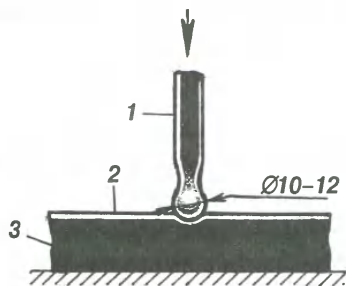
Вытягивание сферы: 1 — чекан; 2 — заготовка; 3 — основа.
